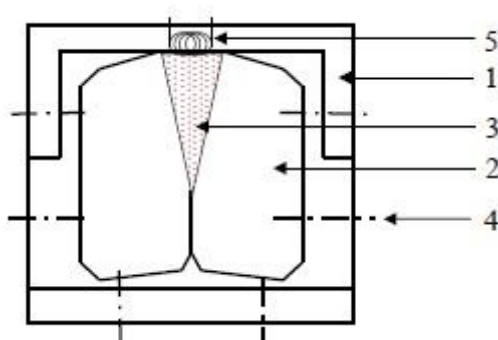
Общий вид сборки клиновой формы 1 – стальная форма; 2 – медный клин; 3 – шихта; 4 – фиксирующие болты; 5 – поджигающая спираль
